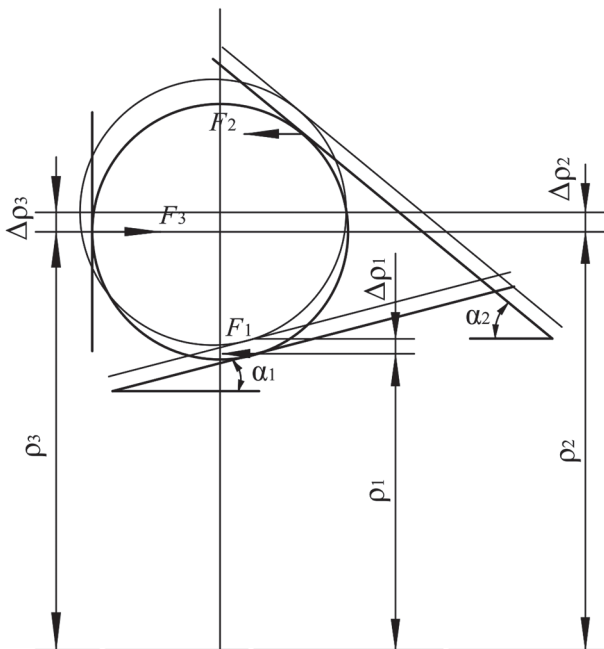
Кинематическая схема одноступенчатого планетарного шарикового редуктора:
